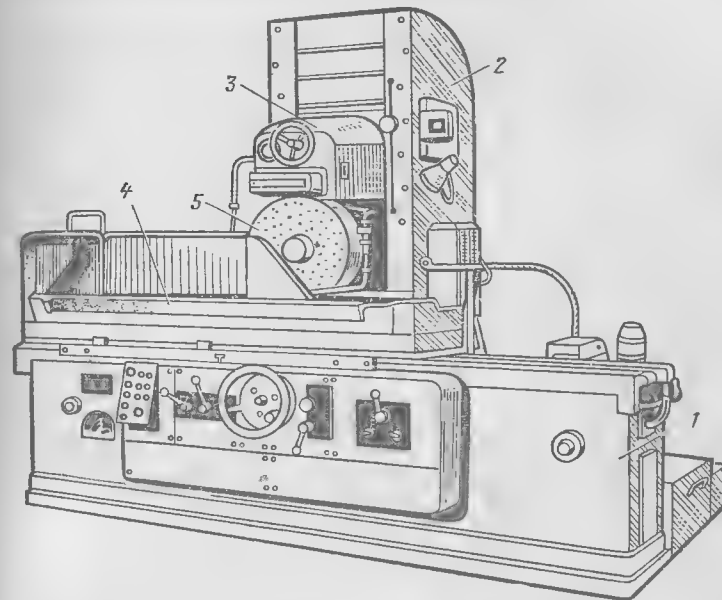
Общий вид плоскошлифовального станка с прямоугольным столом.
